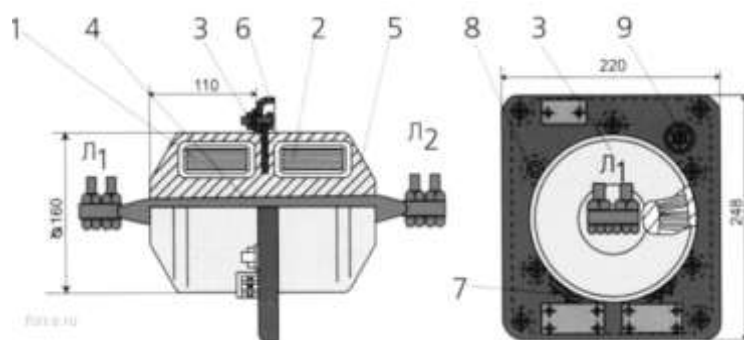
Трансформатор струму Тополь-10: 1 і 2 - сердечники; 3 - кріпильний кільце; 4 - стержень первинної обмотки; 5 - литий корпус; 6 - опорний фланець; 7 - виводи вторинних обмоток; 8 - виступи кріпильного кільця; 9 - заземлюючий болт
